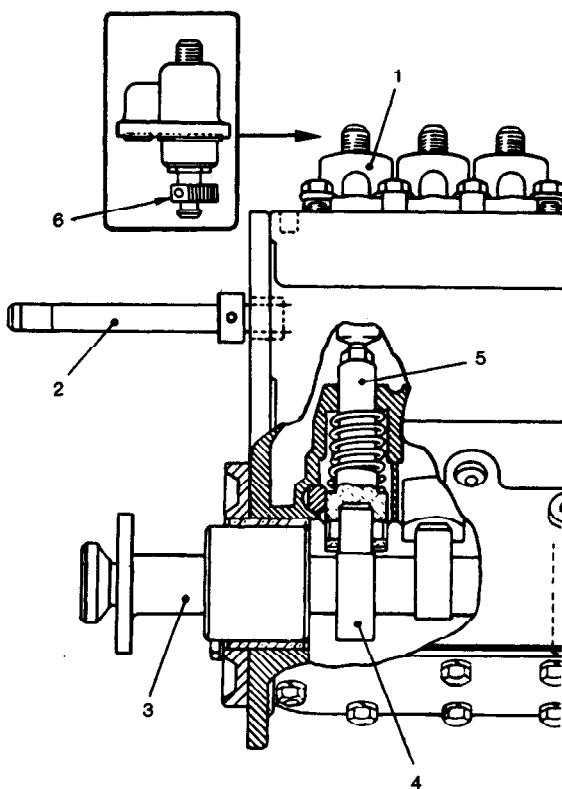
Corte de una bomba de inyección con cuerpo forjado: 1 unidad de bombeo, 2 cremallera, 3 árbol de levas, 4 leva, 5 levántador, 6 sector de engrane
